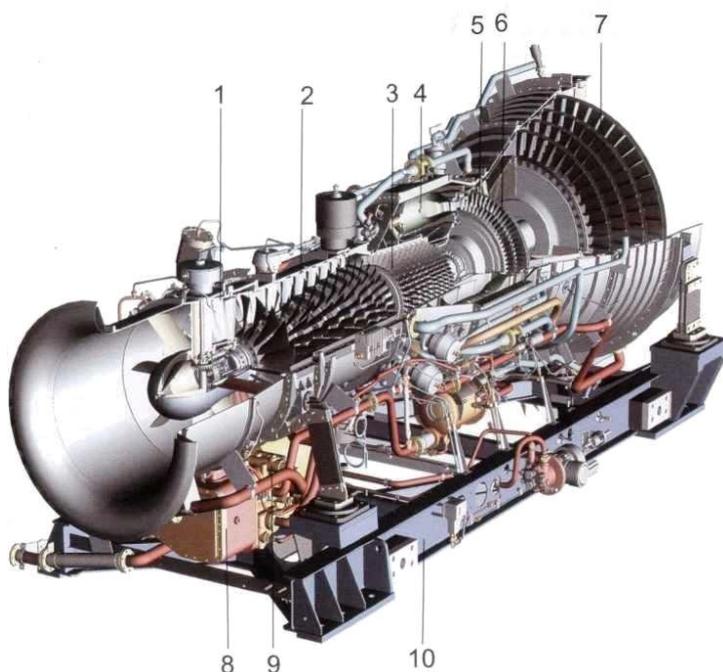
конструкция газотурбинного двигателя НК-16-СТ
